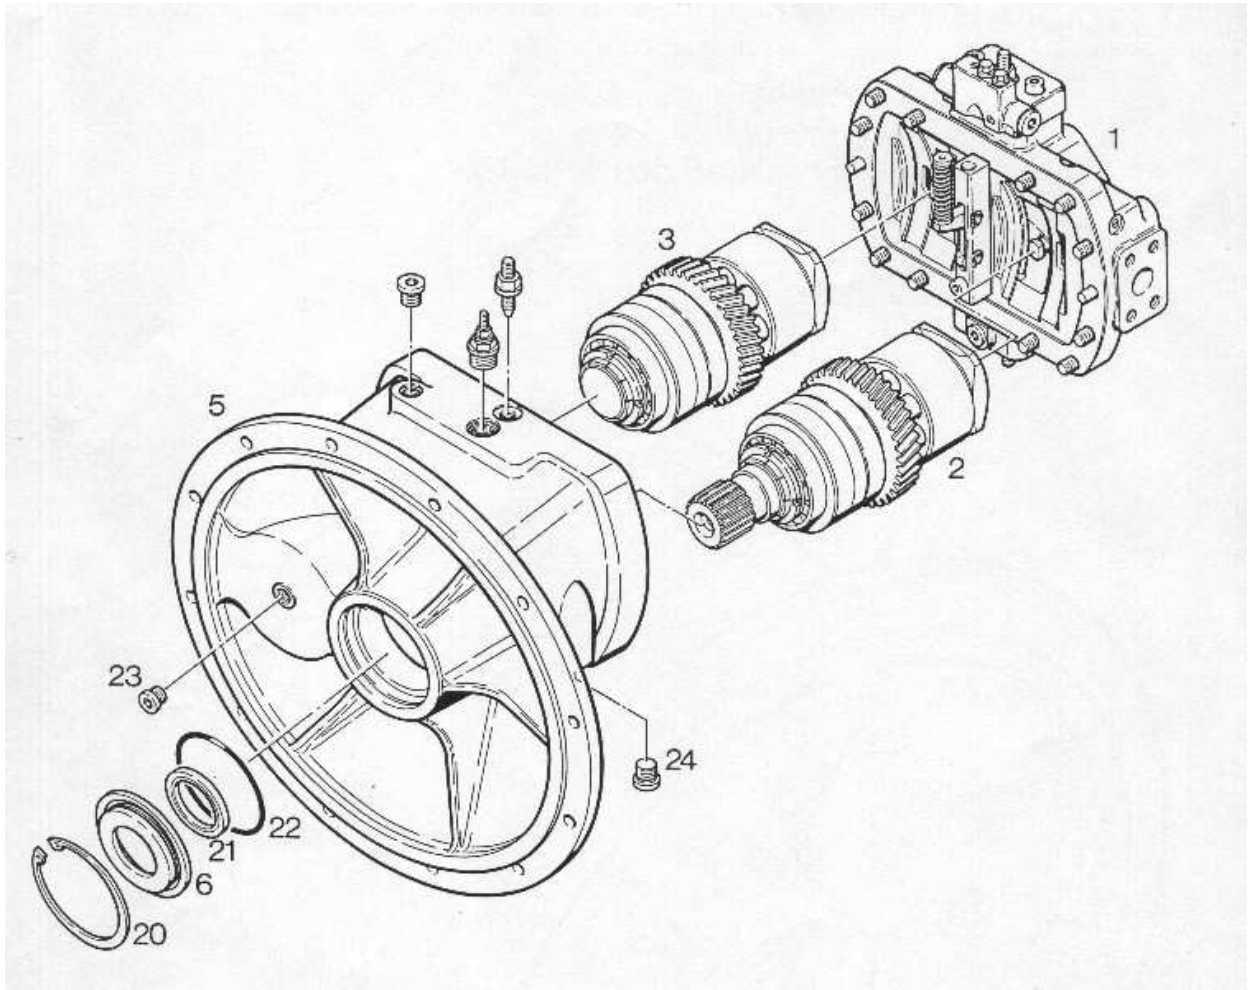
Vue éclatée de la pompe double à cylindrée variable
